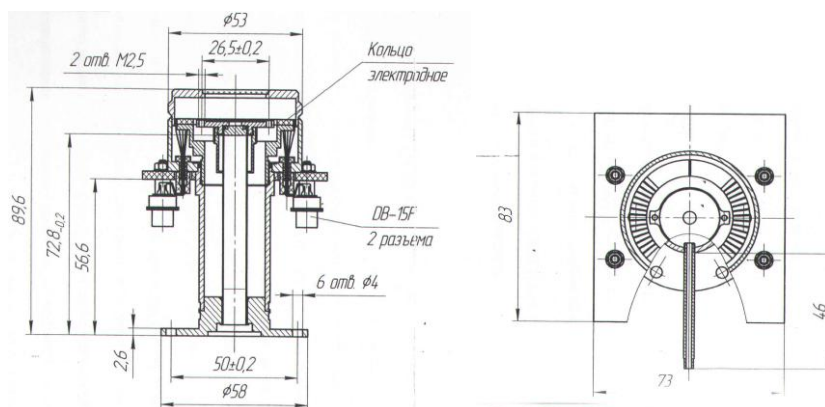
Чертеж корпуса криостата НП79-000.ТУ.
